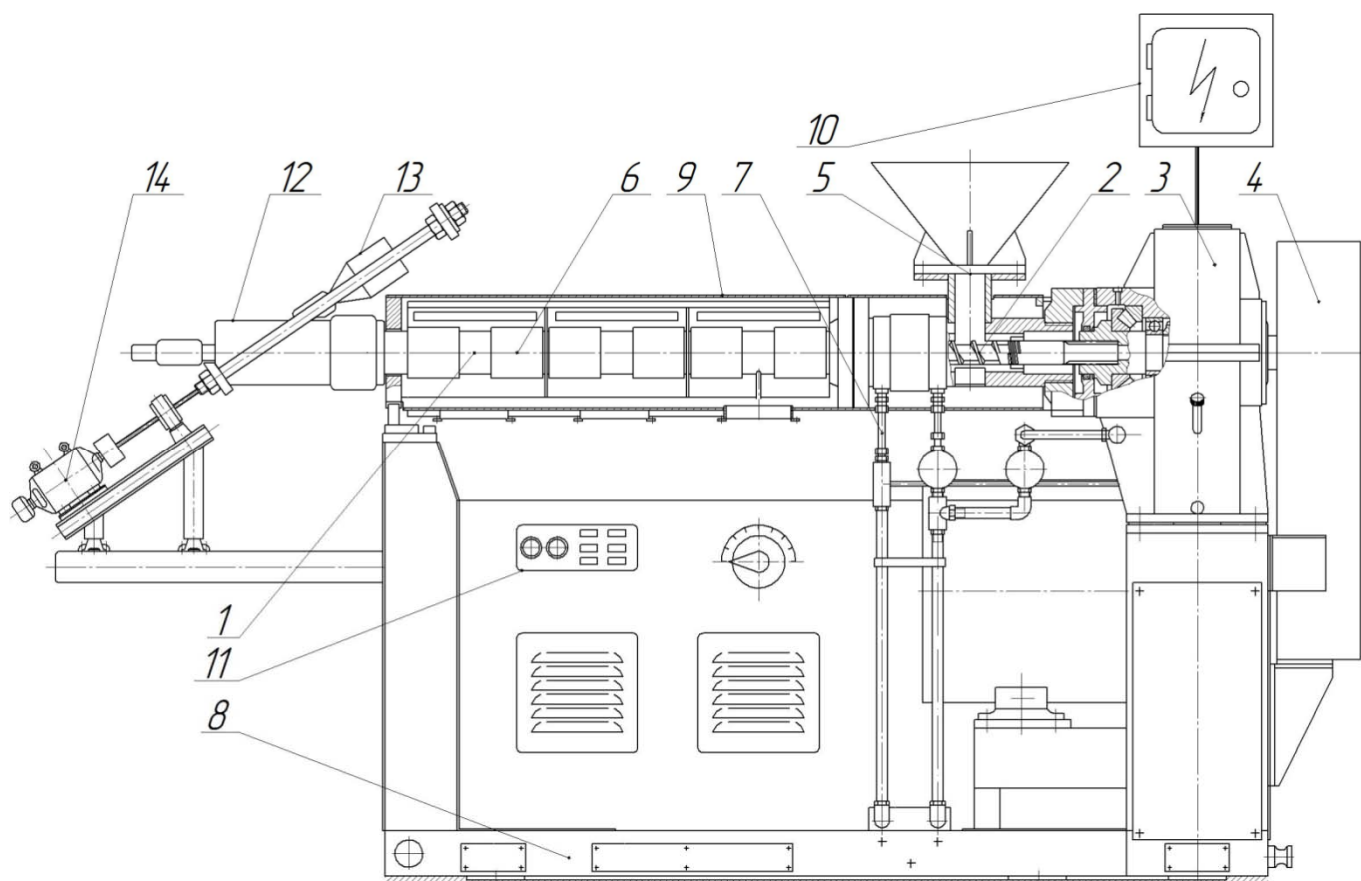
Черв'ячний прес ЧП32x20
